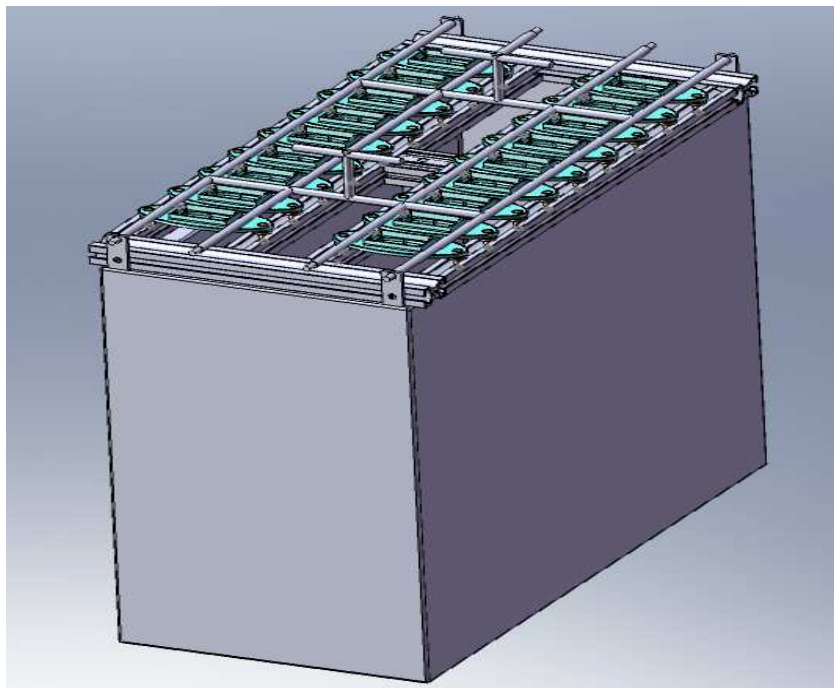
Assembly base gabarit psi (c/ cablagem)
